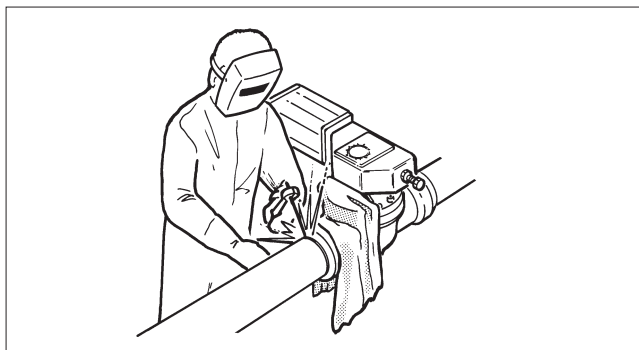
Corps de vanne recouvert d'un tissu de protection humide pendant le soudage
